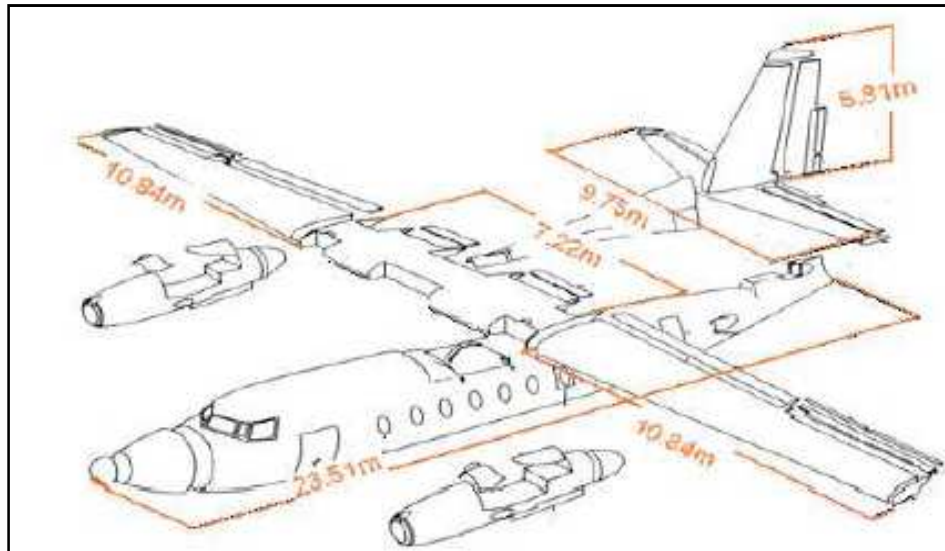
Partes desmontables y dimensiones del avión Fairchild Hiller FH-227J⁷
